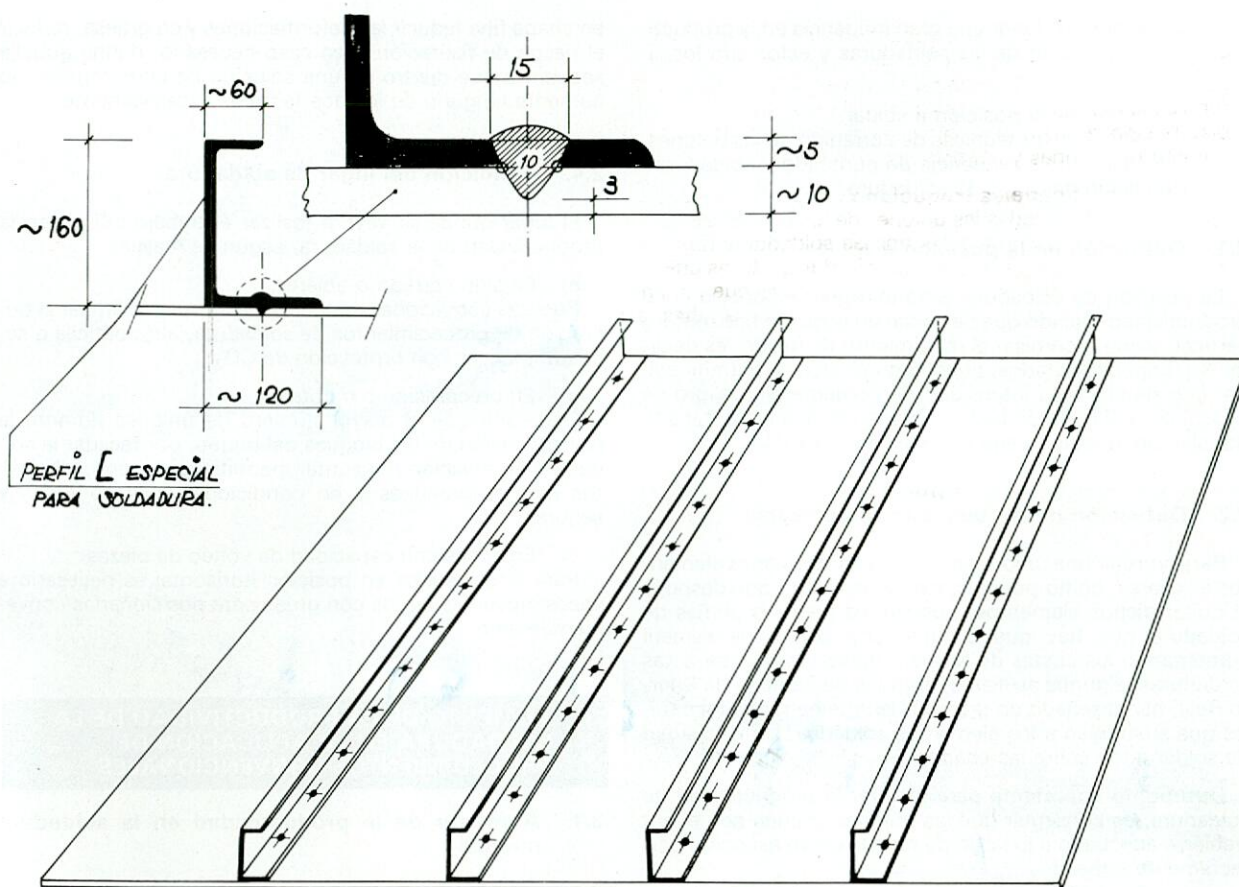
Soldadura por puntos de refuerzos para reducir deformaciones
